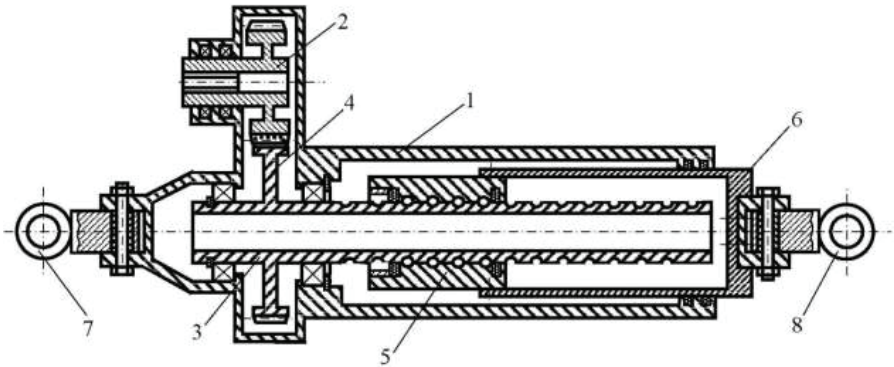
Конструктивная схема шарико-винтового механизма, где 1- корпус; 2- входной вал; 3- ходовой винт; 4- шестерня; 5- шариковая гайка; 6- выходной вал; 7,8- проушина
